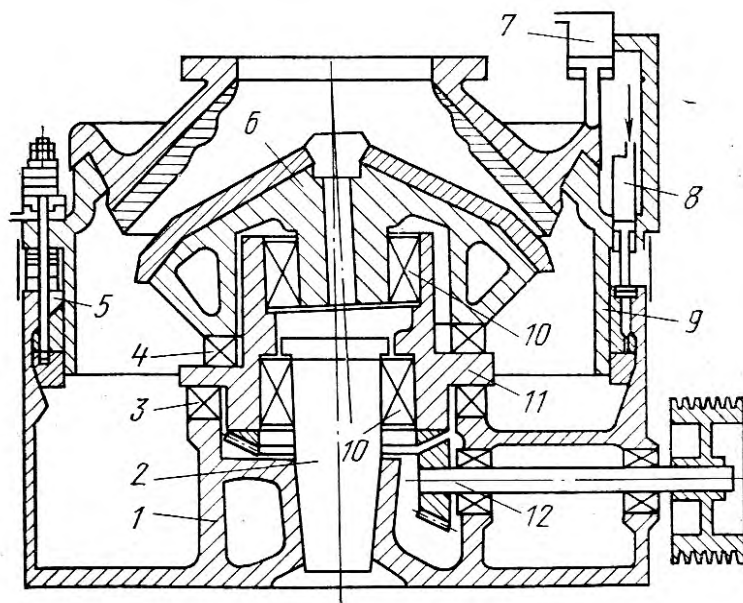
Схема конусной дробилки мелкого дробления с неподвижной осью с подшипниками качения:
